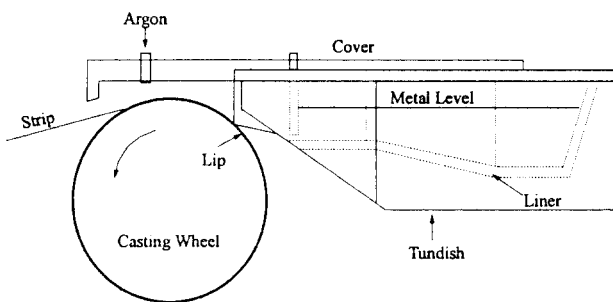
Schematic Sketch of the Single Roll Strip Casting Process
